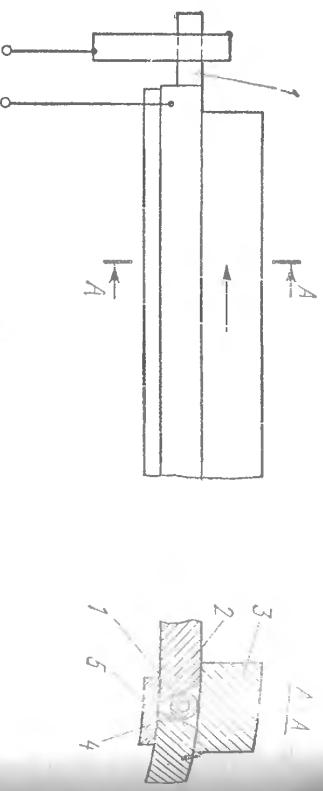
Схема сварки лежачим электродом:
